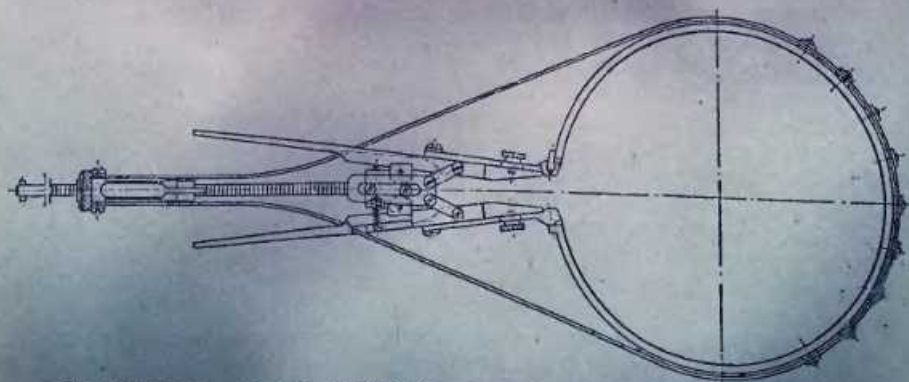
Приспособление JM9690-517 для снятия и постановки поршневых колец
